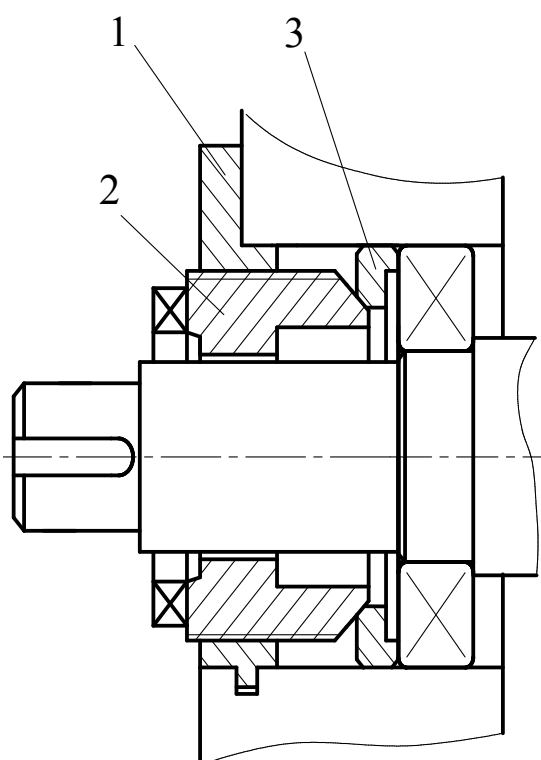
Пример устройства регулирования подшипникового узла
